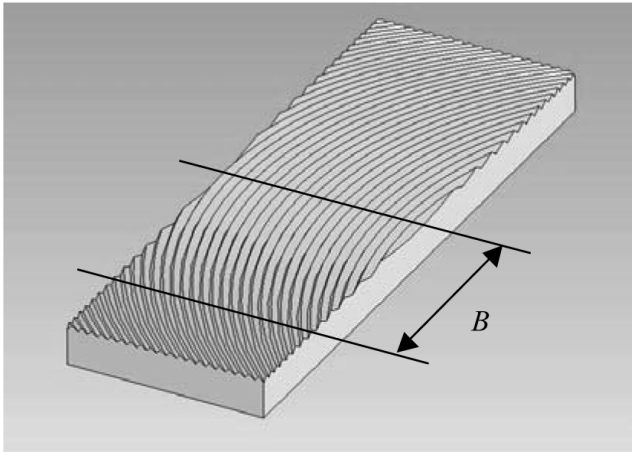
3-D модель поверхні після торцевого фрезерування
